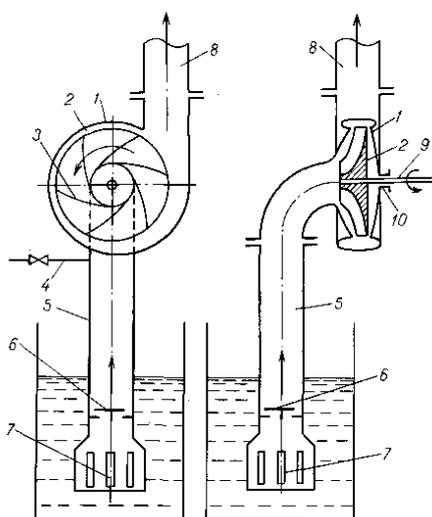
Центробежный консольный насос: 1 – корпус; 2 – рабочее колесо; 3 – лопатки; 4 – линия для залива насоса перед пуском; 5 – всасывающий трубопровод; 6 – обратный клапан; 7 – фильтр; 8 – нагнетательный трубопровод; 9 – вал; 10 – сальник.
